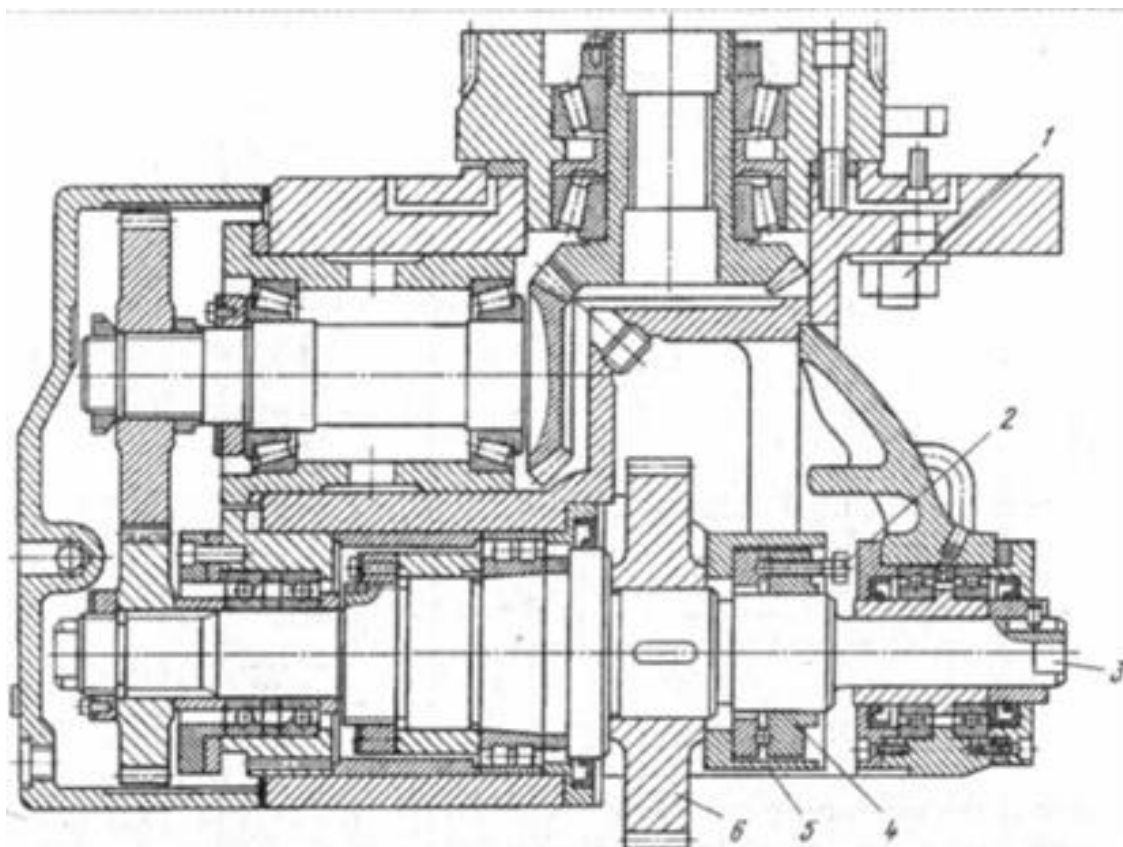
Зубошевнговальная головка станка модели 5B702B
